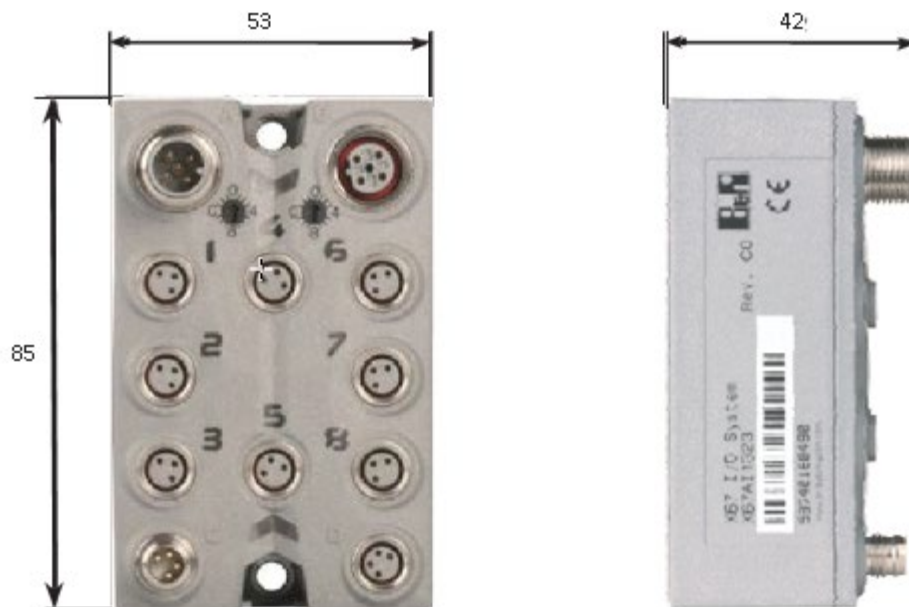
A. Dimensioni del blocco I/O di espansione (millimetri).
